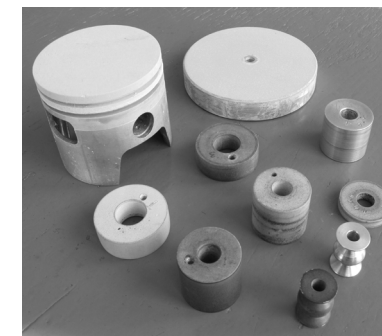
Образцы с покрытием и заготовки для нанесения покрытий.
